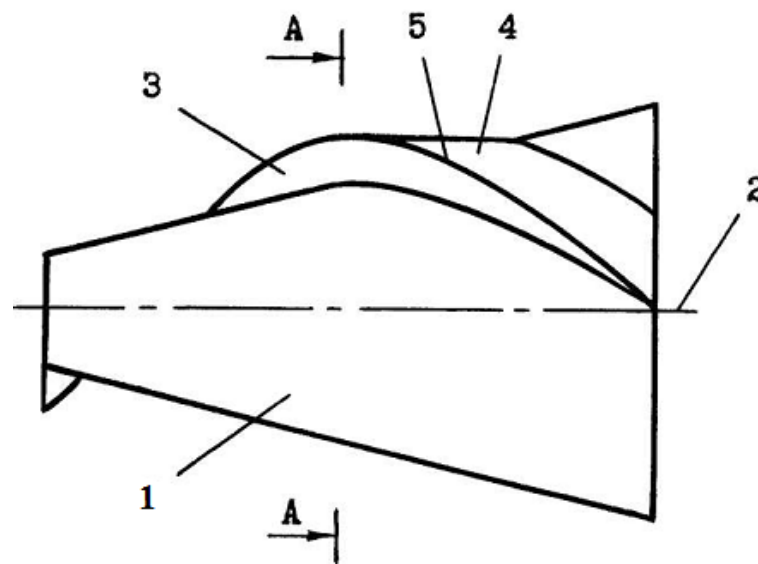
Конструкція ротору Оніпко: 1- конусоподібний корпус, 2 – вісь конуса, 3 – внутрішня поверхня спіралеподібної лопаті, 4 – зовнішня поверхня, 5 – ребро лопаті.
